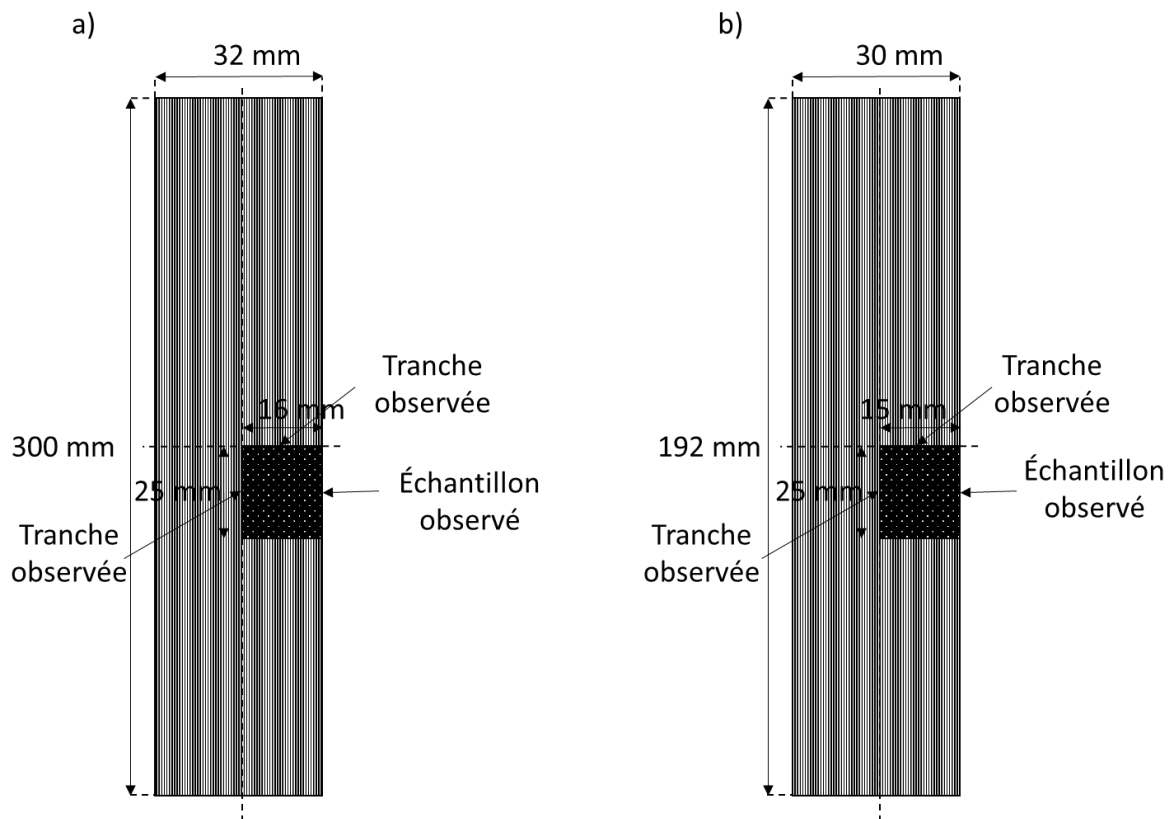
a) Éprouvette de traction et b) Éprouvette de flexion pour l'étude de l'endommagement
